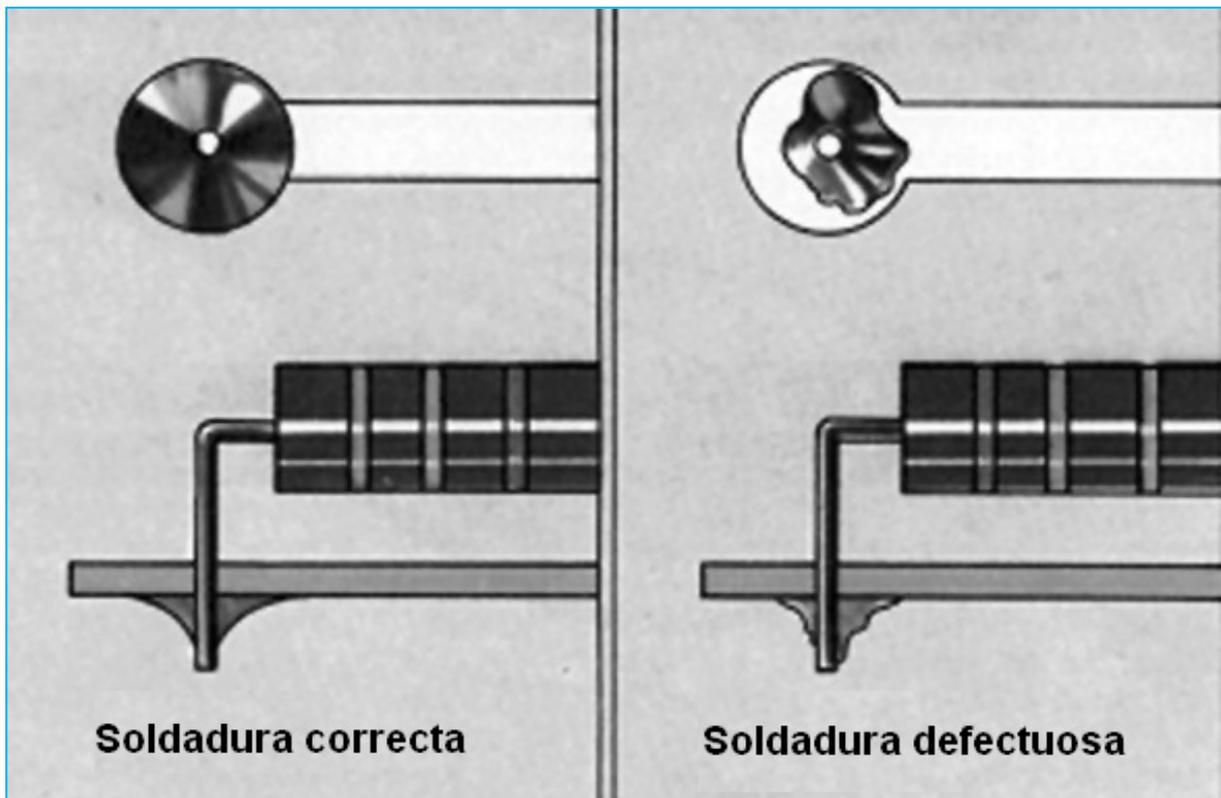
Soldadura del terminal de una resistencia en un circuito impreso. A la izquierda se puede observar, visto en corte de sección y desde arriba, el aspecto final una soldadura realizada correctamente. A la derecha se muestra el aspecto de una soldadura que no presenta las condiciones adecuadas.
